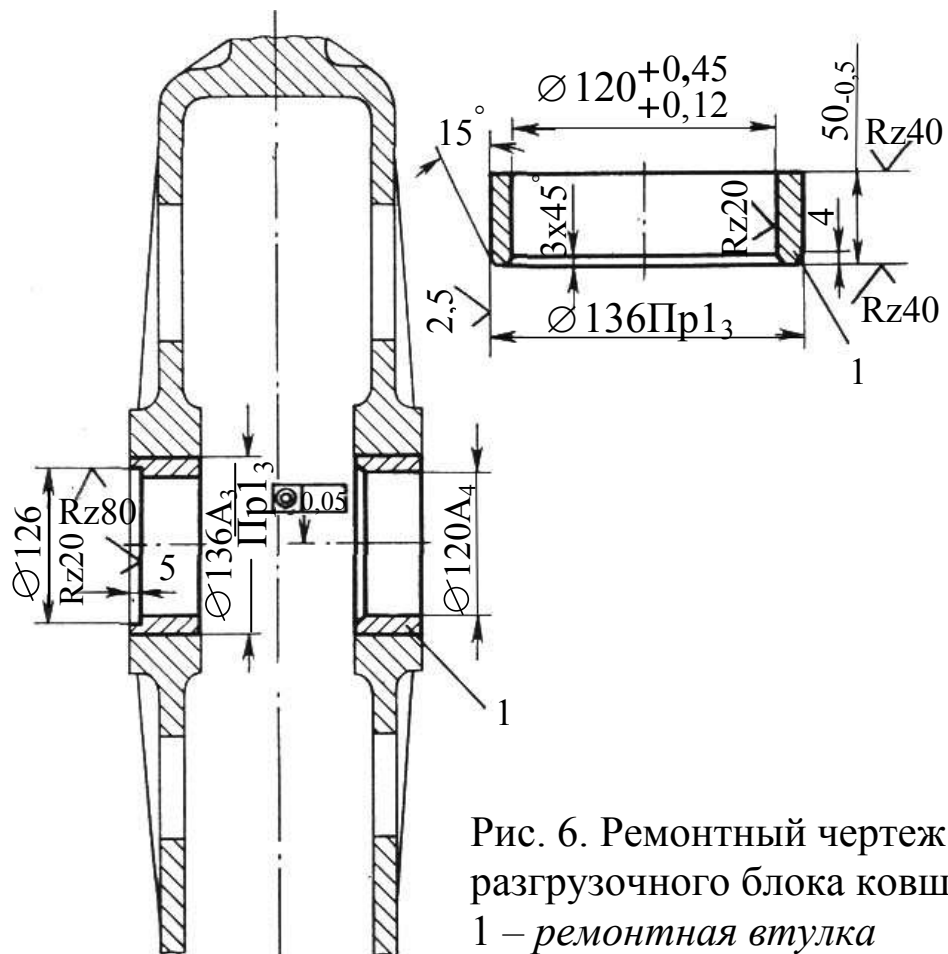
Ремонтный чертеж обоймы разгрузочного блока ковша:
